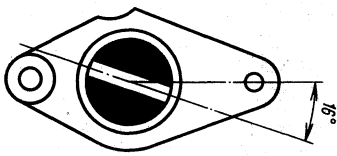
Положение привода прерывателя-распределителя автомобиля «Москвич-412» перед установкой
